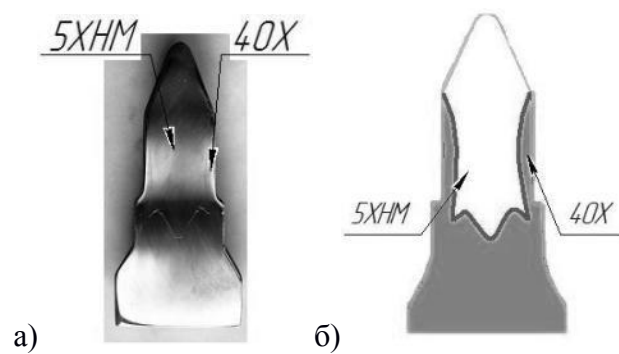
Вид биметаллического образца после деформации реальный образец (а) и модели (б)
